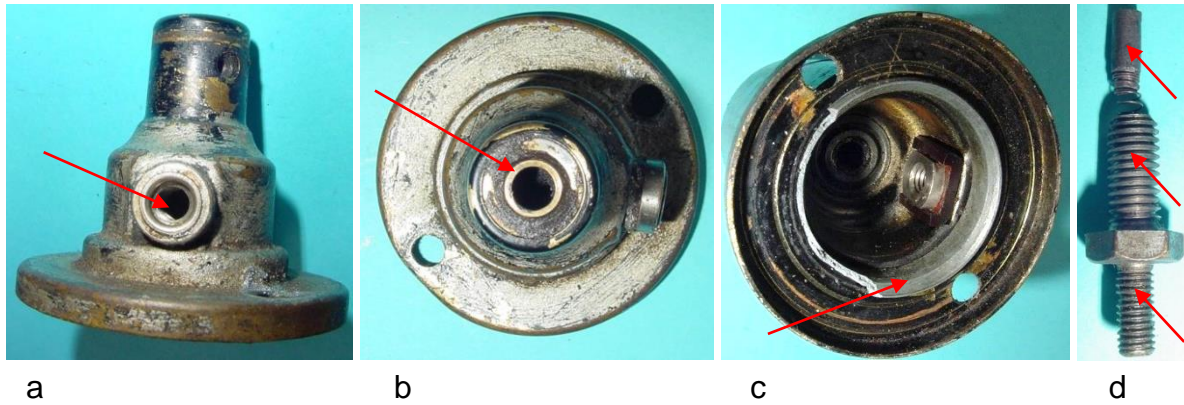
Messinglagerhals: a) Gewindebohrung für den Kabelanschlussbolzen, b) 18 mm langes Gleitlagerrohr, c) Justiering für den Magneten, d) Kabelanschlussbolzen, Bürstenhalter und 3 mm starke Kohlebürste
